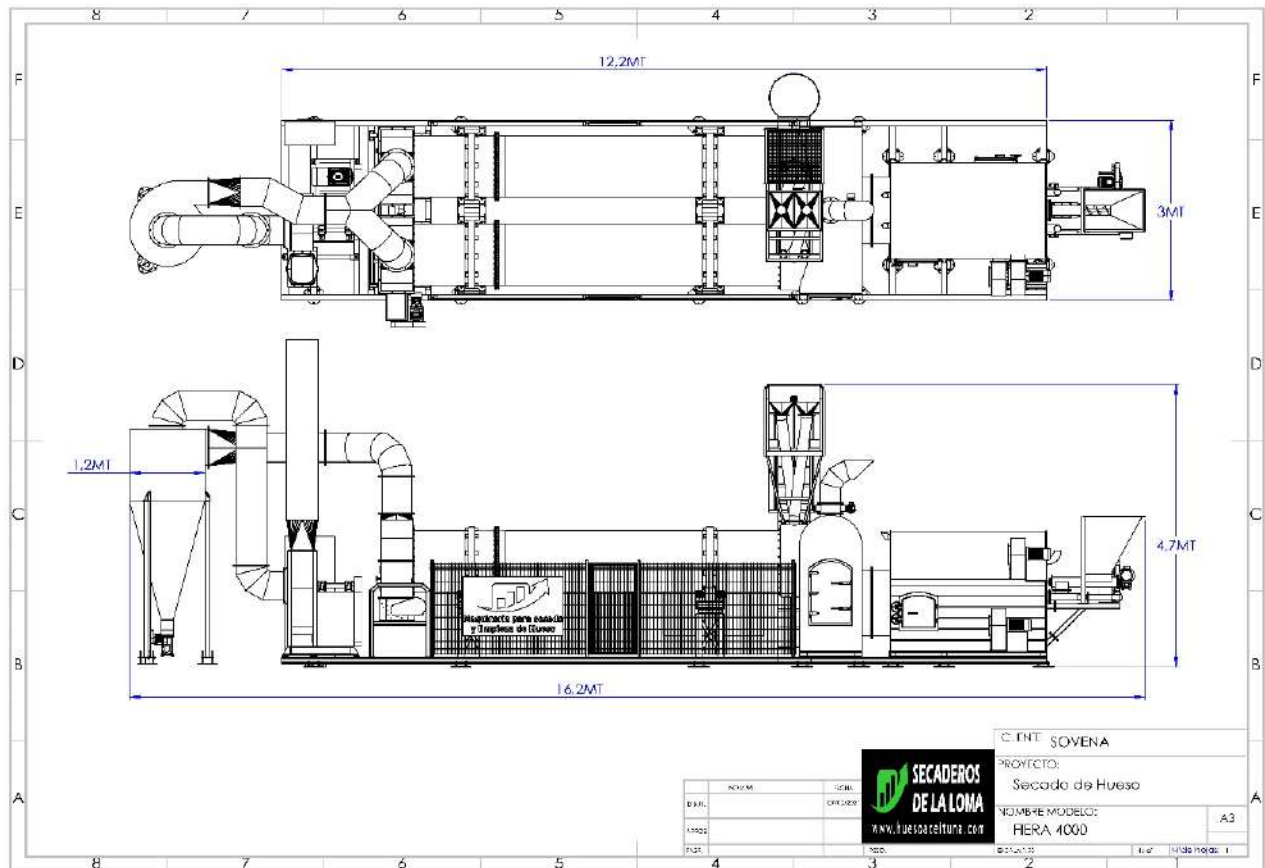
Planta y alzado de modelo fiero 4000 en Almazara. Fuente: Secaderos la Loma. 2023.
